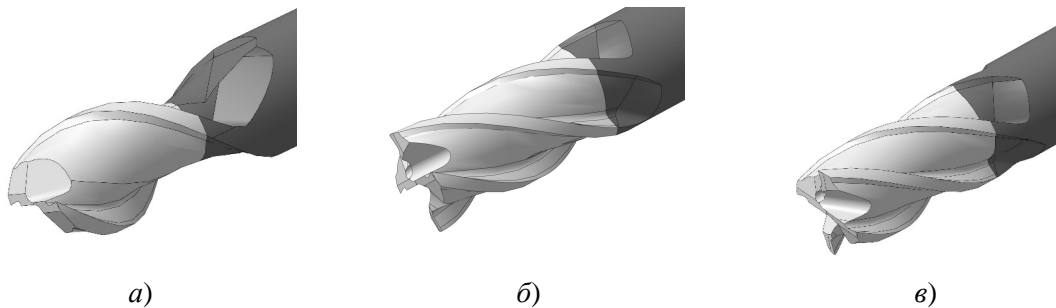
3D-модели фрез: а – с двумя режущими зубьями; б – с увеличенным диаметром; в – с углом винтовой канавки равной 38°
